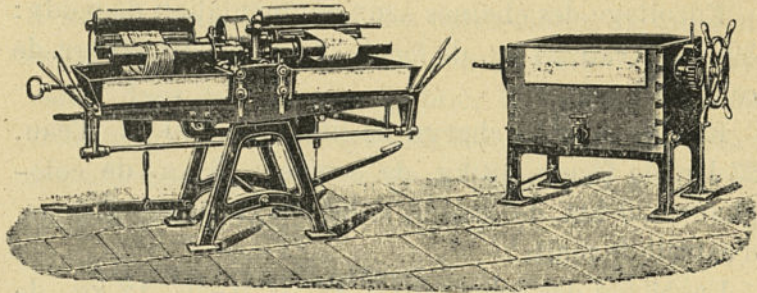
Machine à encoller et machine à tordre les écheveaux
